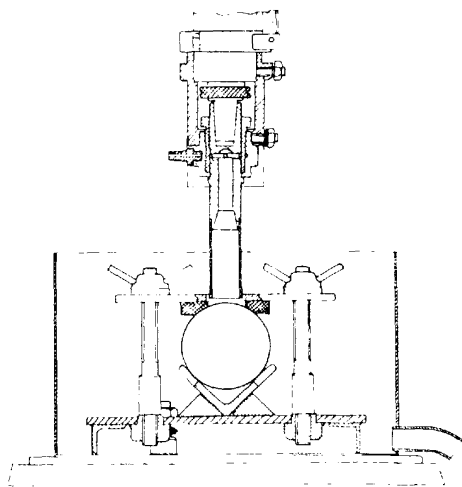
Приспособление к сверлильному станку для изготовления цилиндрических образцов с помощью алмазно-абразивного инструмента /В.П.Потапов, 1975/.
